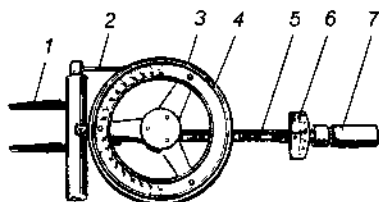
Прибор КИ-4832 для проверки углового зазора трансмиссии: 1 — губка зажима; 2 — вороток; 3 — диск со шкалой; 4 — полукольцо с подкрашенной жидкостью в полиэтиленовой трубке; 5 — стрелка; 6 — шкала динамометрической рукоятки; 7 — динамометрическая рукоятка
